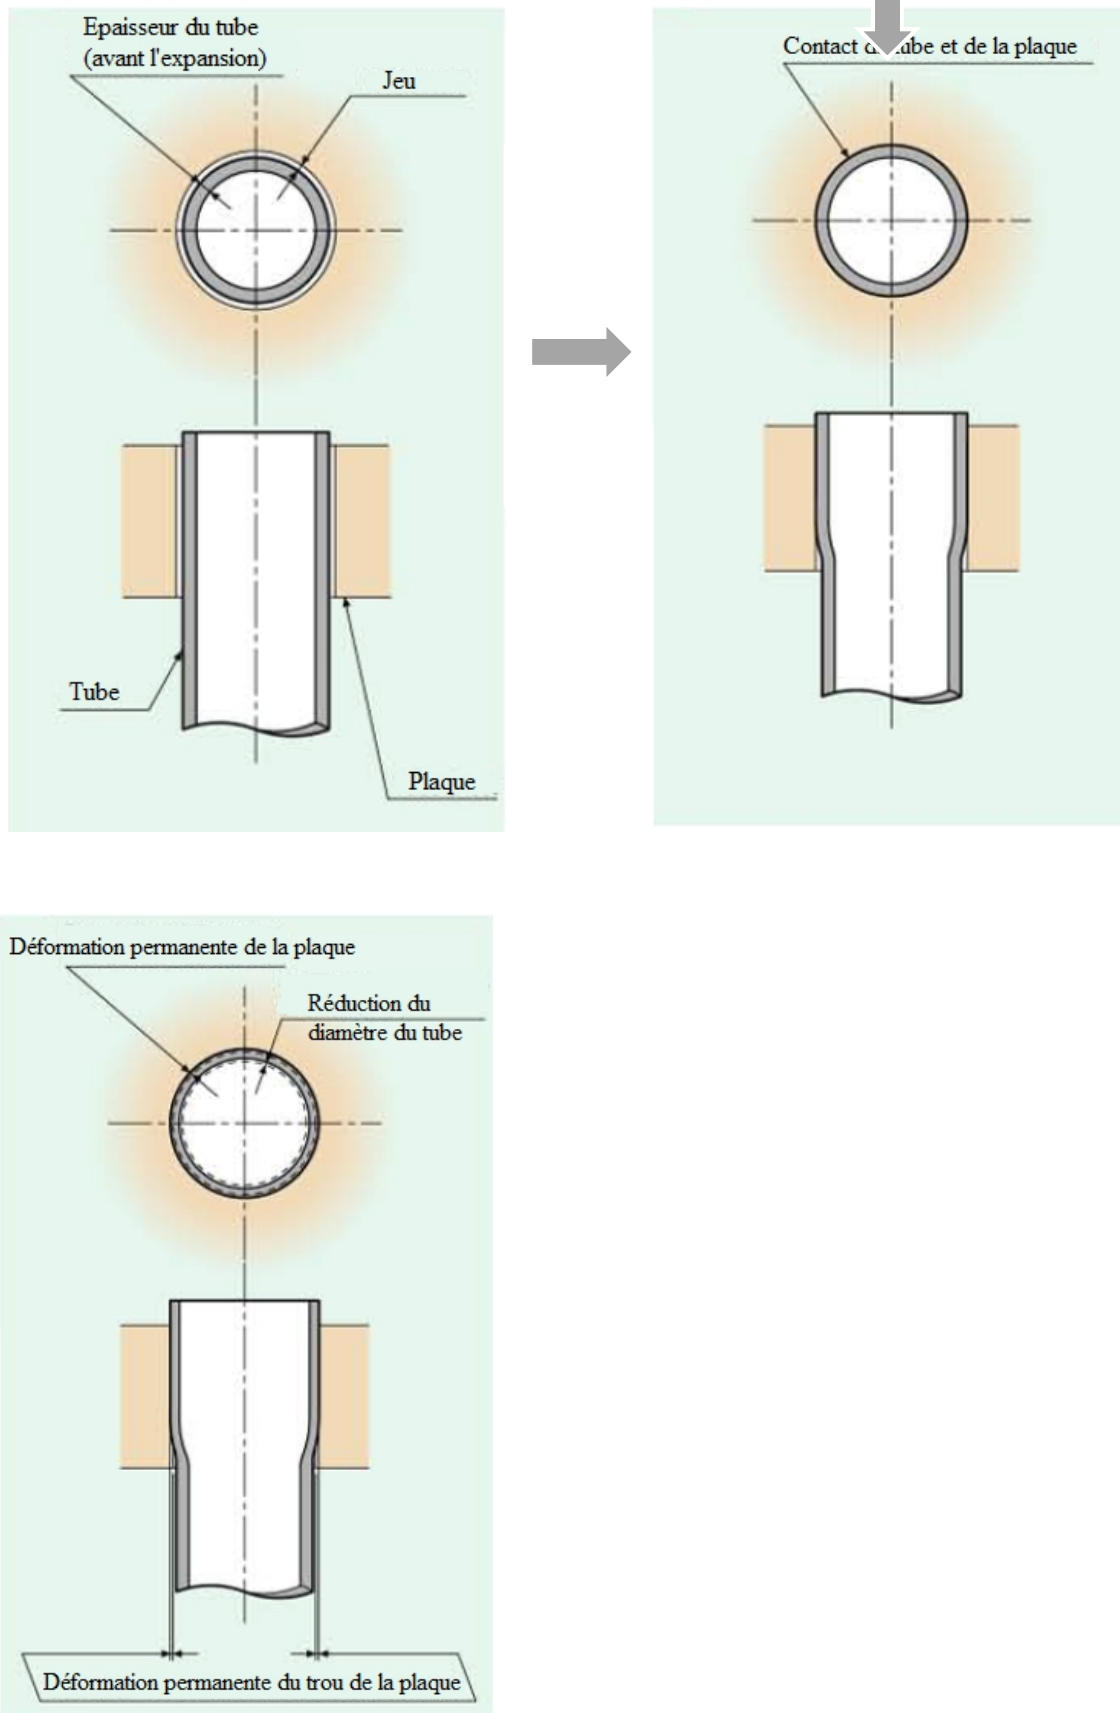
Assemblage d'un tube et d'une plaque par dudgeonnage [6]
